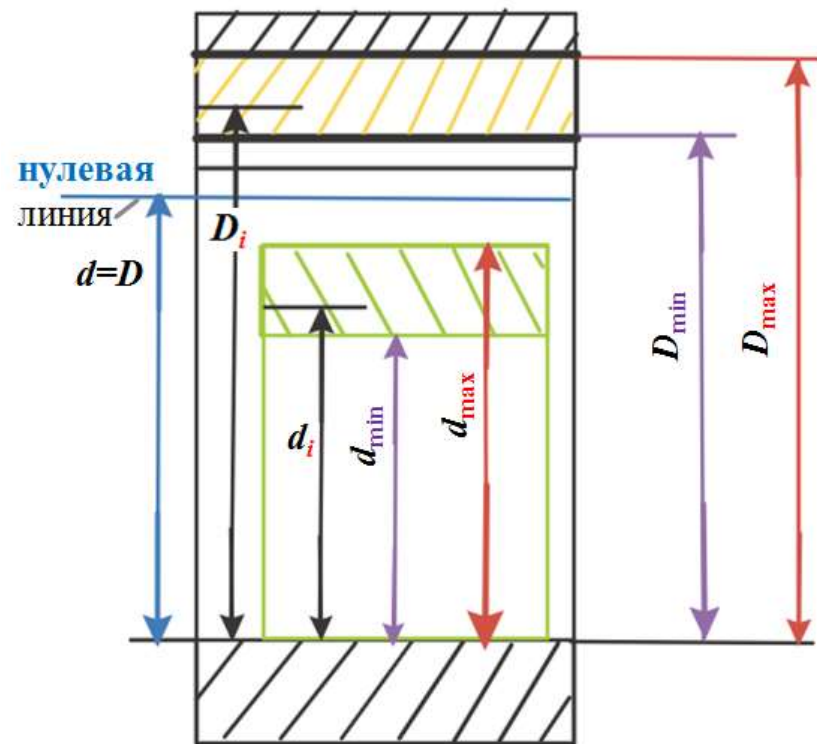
Положение полей допусков гладкого соединения
